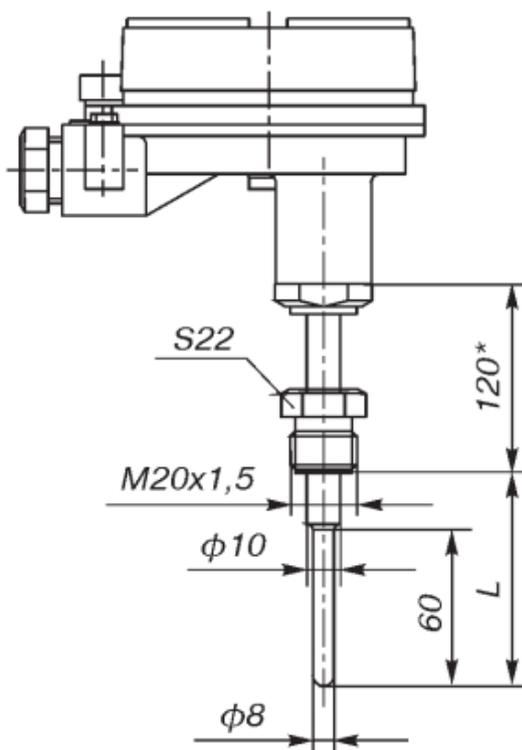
Габаритные и присоединительные размеры Метран-288
